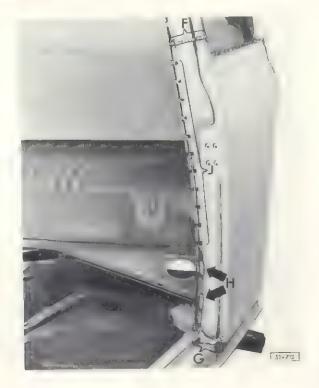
Seitenteil außen – Teilstuck einschweißen.
